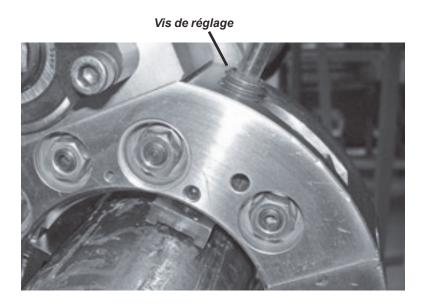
Tournez la vis de réglage pour serrer ou desserrer la cale d'appui.
